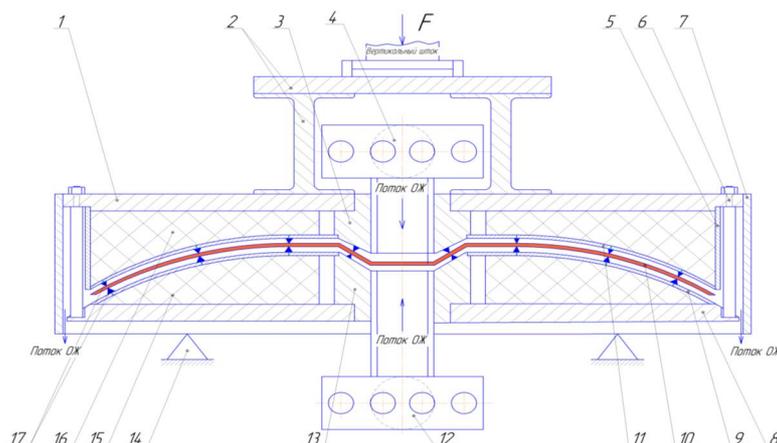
Принципиальная схема устройства закалочного охлаждения дисков: 1-плита верхняя; 2-фланец; 3-вставка верхняя; 4-коллектор верхний; 5-кожух внутренний; 6-упор; 7-кожух наружный; 8-плита нижняя; 9-матрица; 10-заготовка диска; 11-пуансон; 12-коллектор нижний; 13-вставка нижняя; 14-опора; 15-плита монтажная нижняя; 16-плита монтажная верхняя; 17-фиксатор
